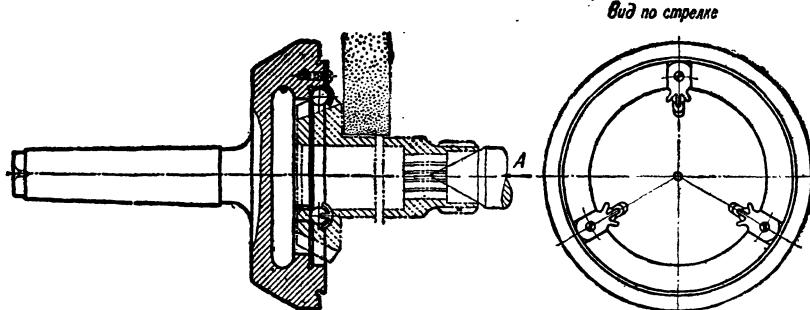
Патрон для шлифовки хвостовика конической шестерни.
